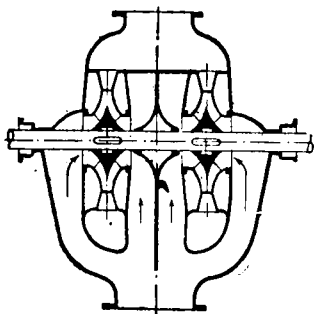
Многоколесный центробежный насос с параллельным соединением колес.
